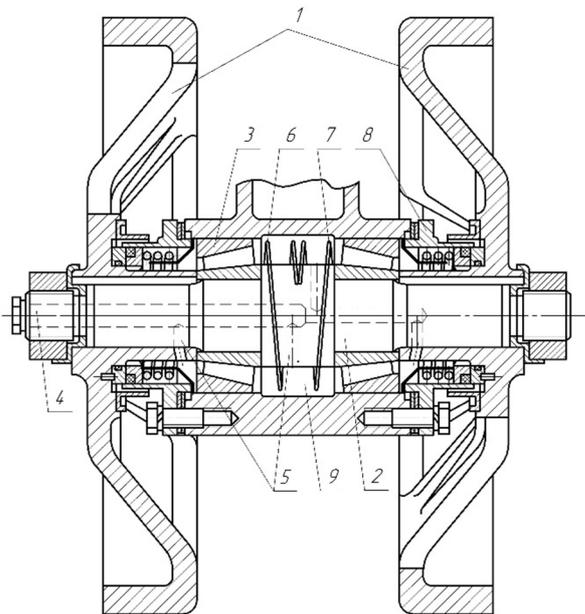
Шнеково-винтовое устройство для обеспечения циркуляционного режима смазывания:
